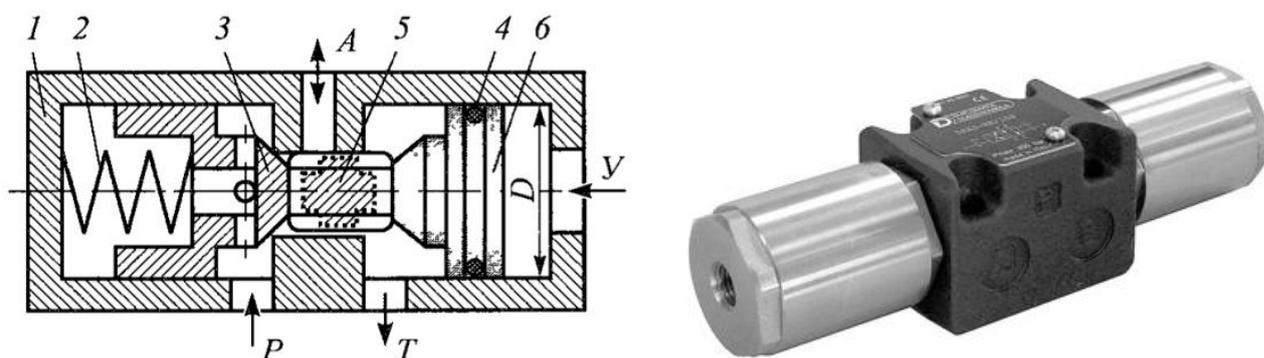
Конструктивная схема направляющего клапанного гидрораспределителя 3/2 с гидравлическим управлением
